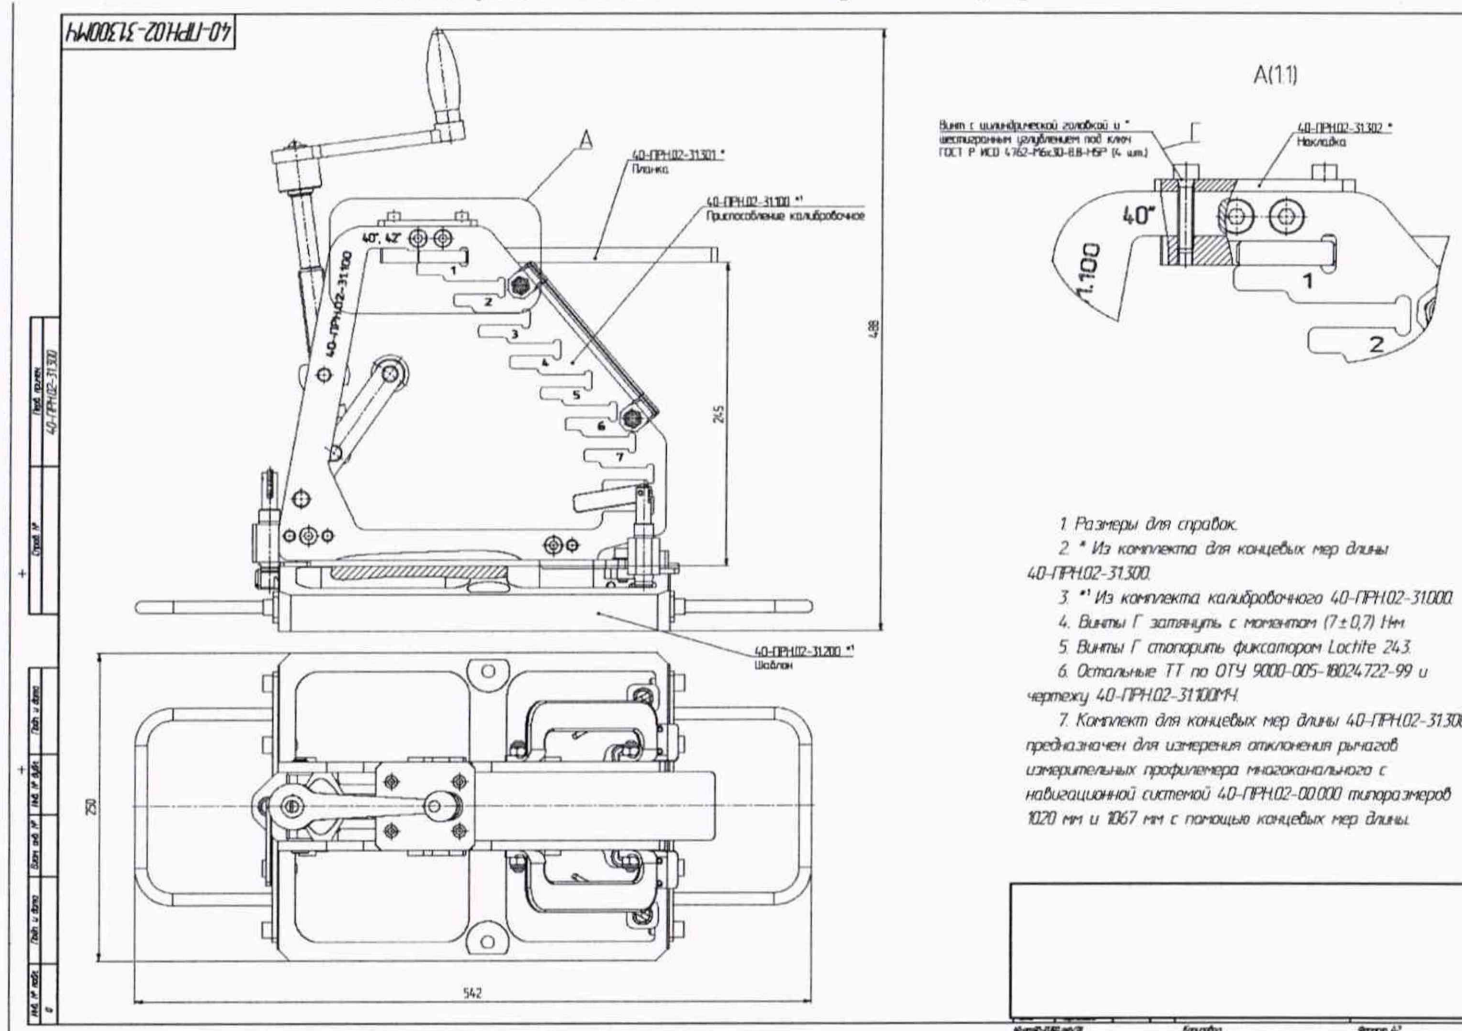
Чертеж планки установленной на калибровочное устройство
